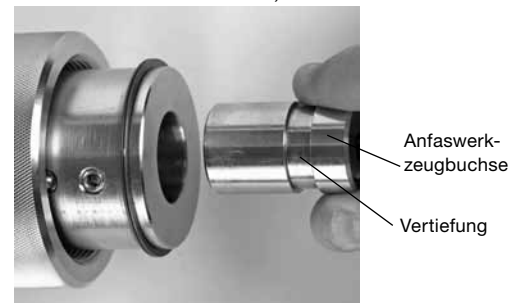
Entfernen/Anbringen der Anfaswerkzeugbuchse
